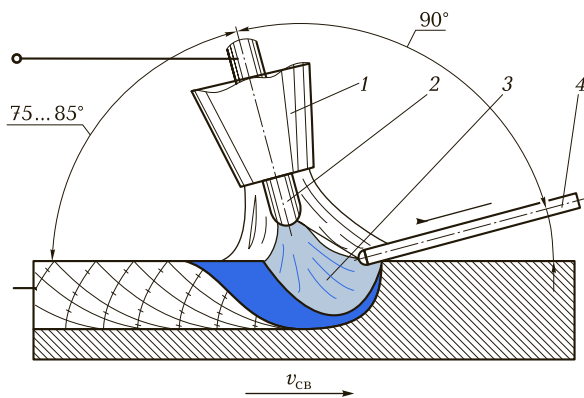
Схема ручной сварки вольфрамовым электродом:
